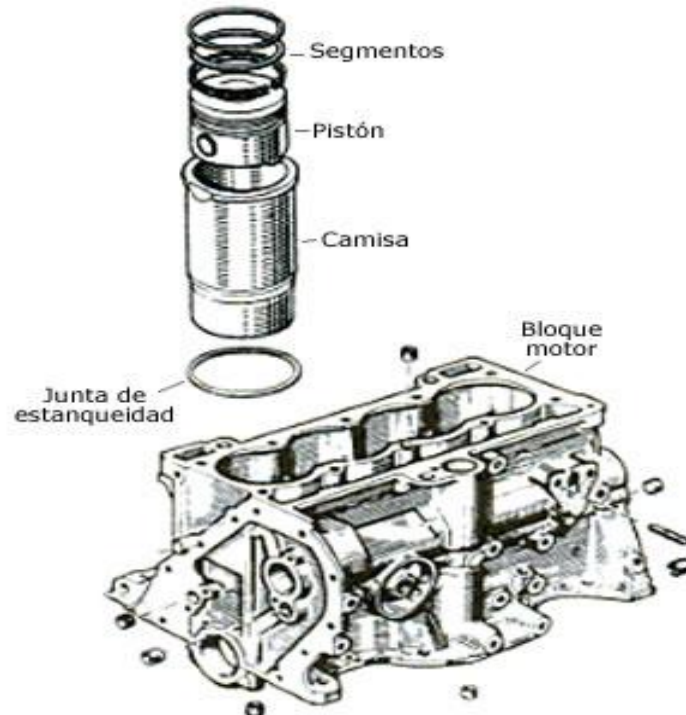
Despiece de Camisa y Bloque de Motor. (Volvo Equipment, 2014)
